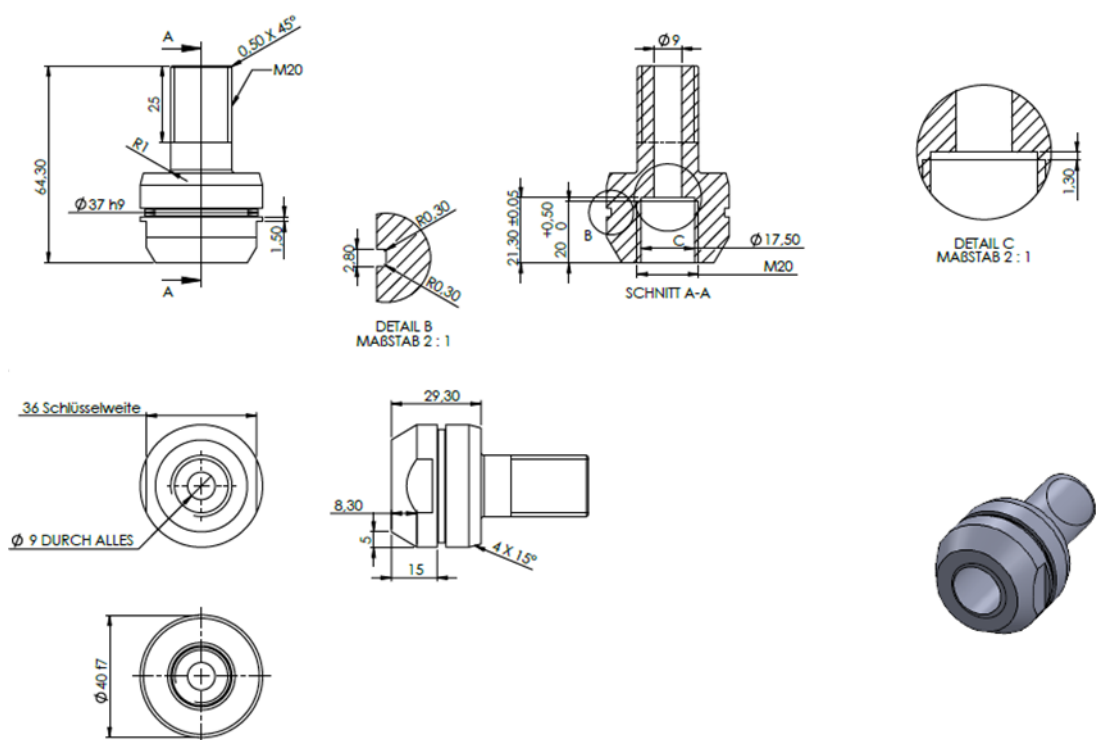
Kolbenstange Endstück unten mit Angaben in mm.
